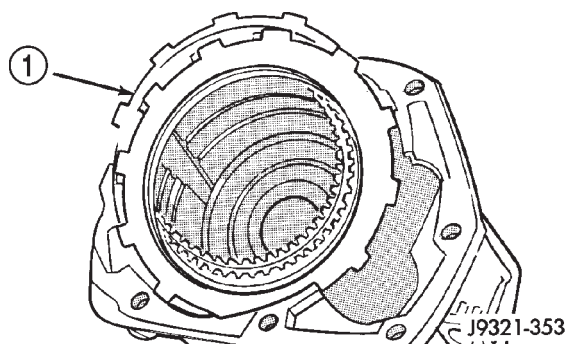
Desmontaje del conjunto de embrague de sobremarcha
